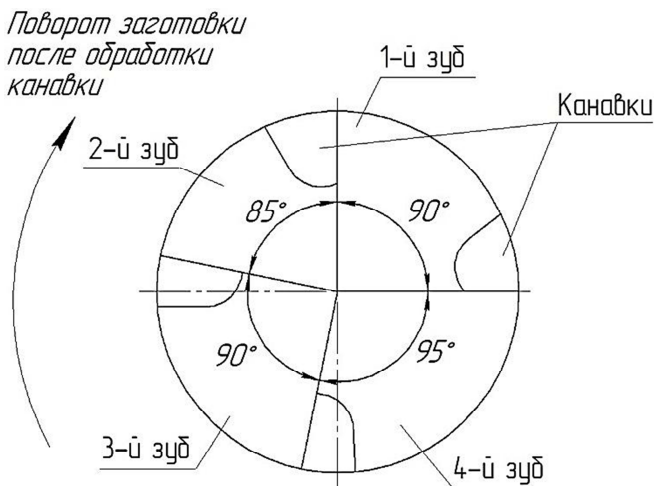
Неравномерная разбивка зубьев инструмента
